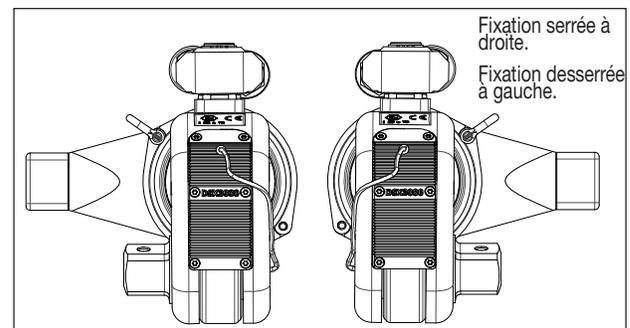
sens du carré conducteur pour le desserrage/serrage
